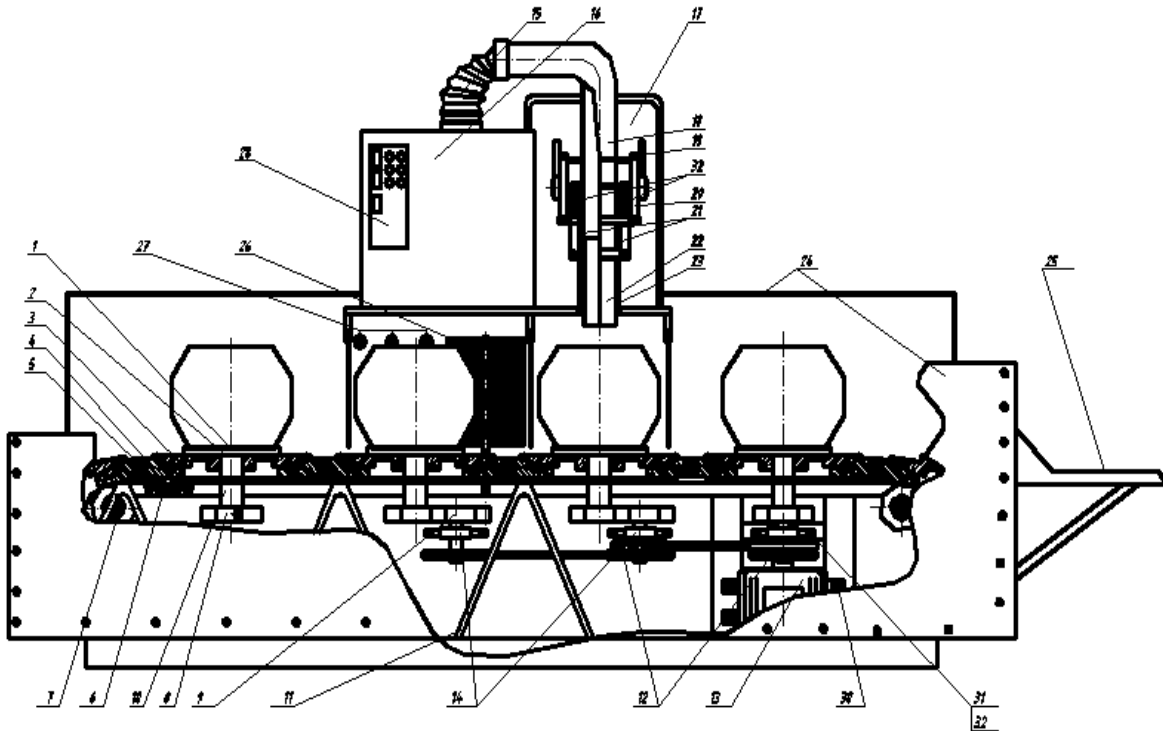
Аппарат для очистки плодов тыквы: 1 – платформа игольчатая; 2 – держатель плодов; 3 – платформа подвижная верхняя; 4 – платформа подвижная нижняя; 5 – передача цепная; 6 – ролики; 7 – ролики транспортерные; 8 – шестерня ведомая; 9 – шестерня ведомая; 10 – вал; 11 – опора; 12 – передача клиноременная; 13 – электродвигатель; 14 – опоры подшипников; 15 – патрубок гофрированный; 16 – установка вакуумная; 17 – привод движущий; 18 – патрубок резиновый; 19 – направляющая верхняя, 20 – направляющие нижняя; 21 – блок ножей гибких; 22 – нож трубчатый внутренний; 23 – нож внешний; 24 – корпус; 25 – лоток разгрузочный; 26 – щетки очищающие; 27 – форсунки; 28 – пульт управления
